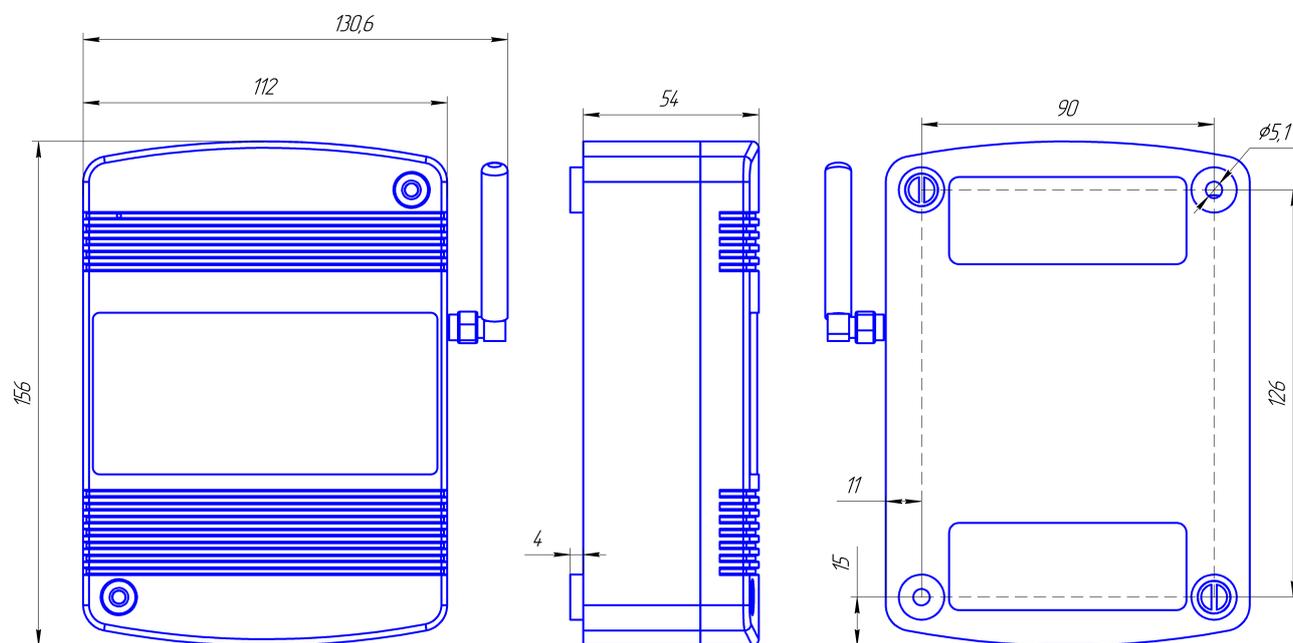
Габаритные и установочные размеры контроллера с креплением на стену
